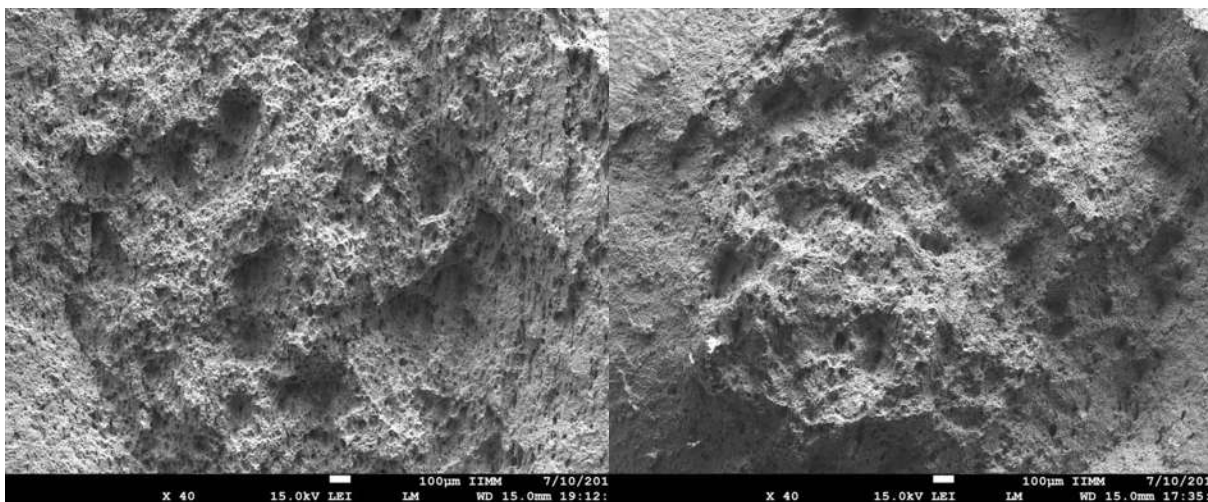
24.- Fractografía de la soldadura 6-1(relevado de esfuerzos, condición 2).
